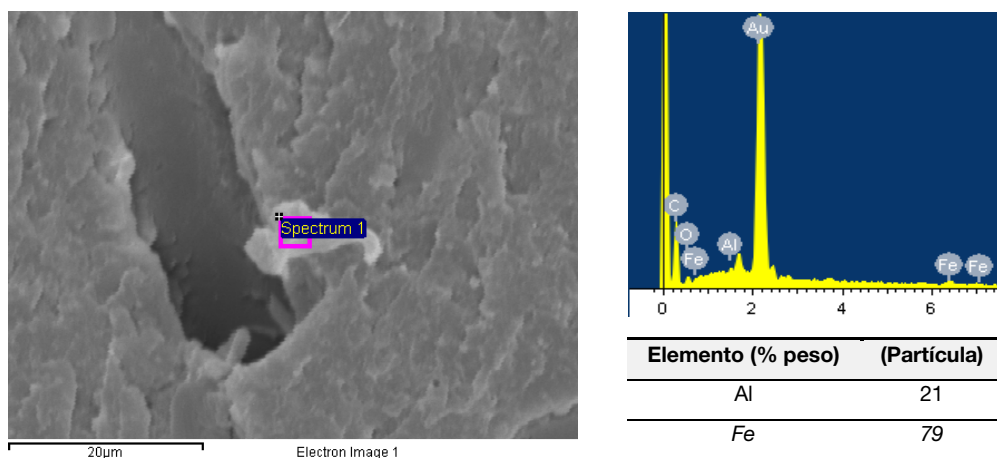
Análisis composicional semicuantitativo de una partícula encontrada en la línea de soldadura de R1V
